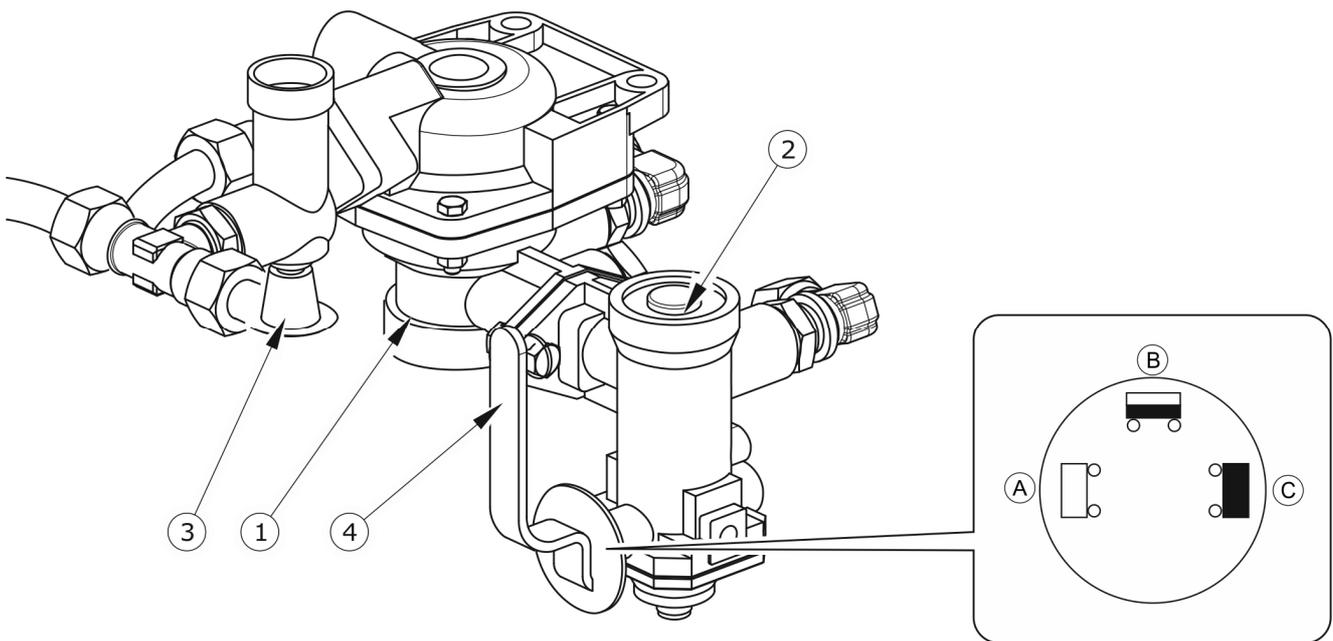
Soupape de commande et régulateur de force de freinage
